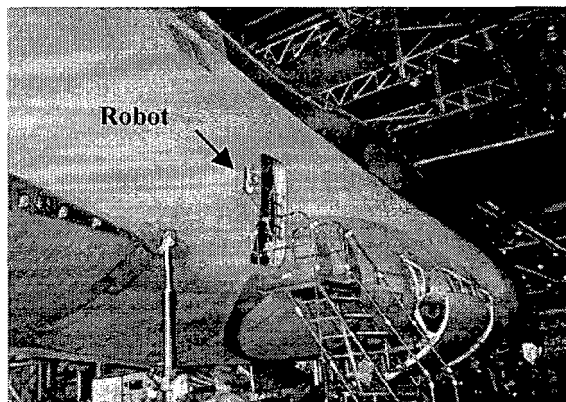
Robot MACS I, realizando una tarea de inspección
